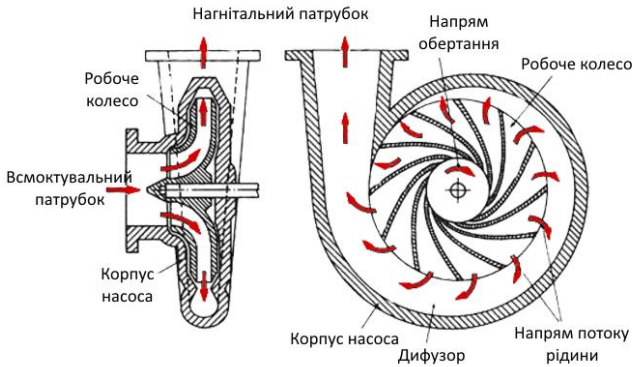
Схема робочого колеса відцентрового насоса
